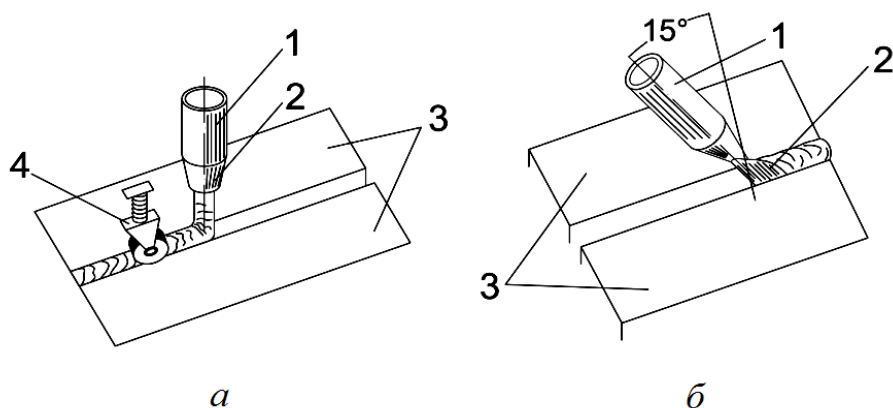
Схема сварки пластмасс экструдированной присадкой:
